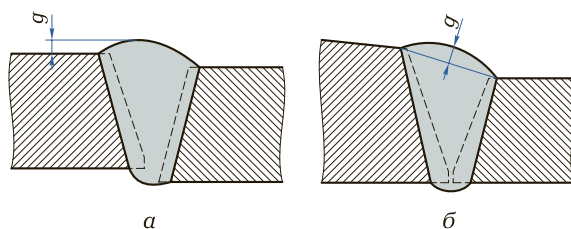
Измерение выпуклости g стыкового шва при разных уровнях лицевых поверхностей деталей, обусловленных их смещением при сборке соединения под сварку (а) и неодинаковой толщиной (б)
